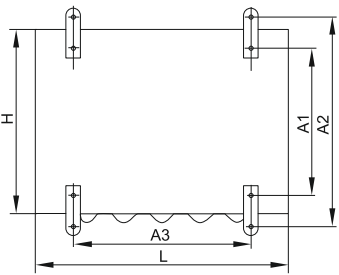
Вид корпуса сзади / Figure 1 – Enclosure back elevation / 1 сурет – Корпусстың артқы көрінісі
